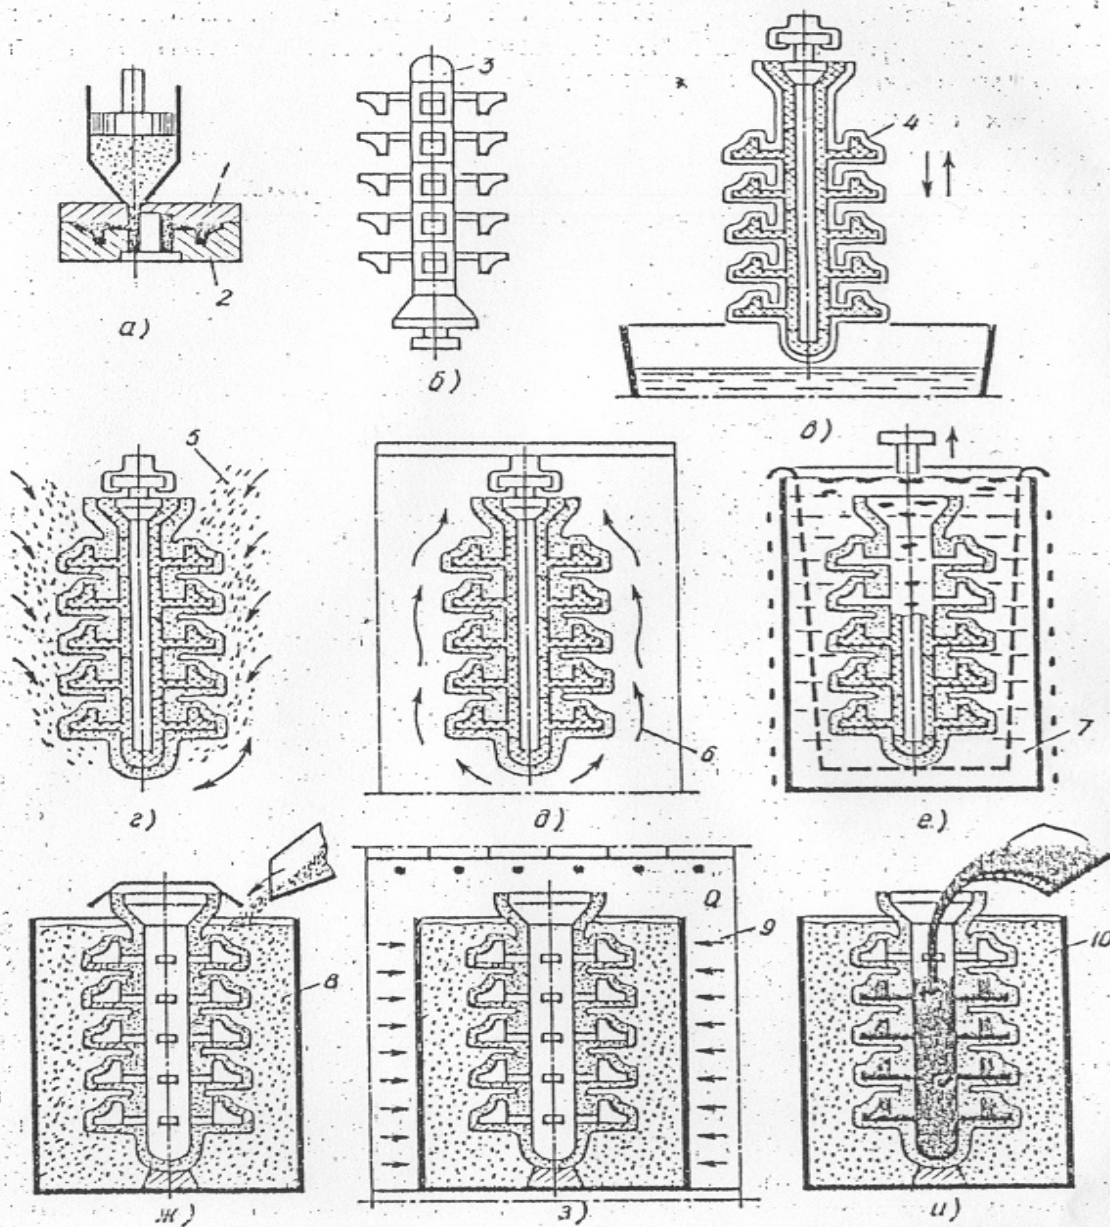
Последовательность изготовления многослойной оболочковой формы по выплавляемым моделям: а - запрессовка модельного состава в пресс-форму; б - сборка блока; в - нанесение суспензии; г - обсыпка; д - сушка; е - удаление модели; ж - засыпка опорным материалом; з - прокатка; и - заливка формы расплавом.
